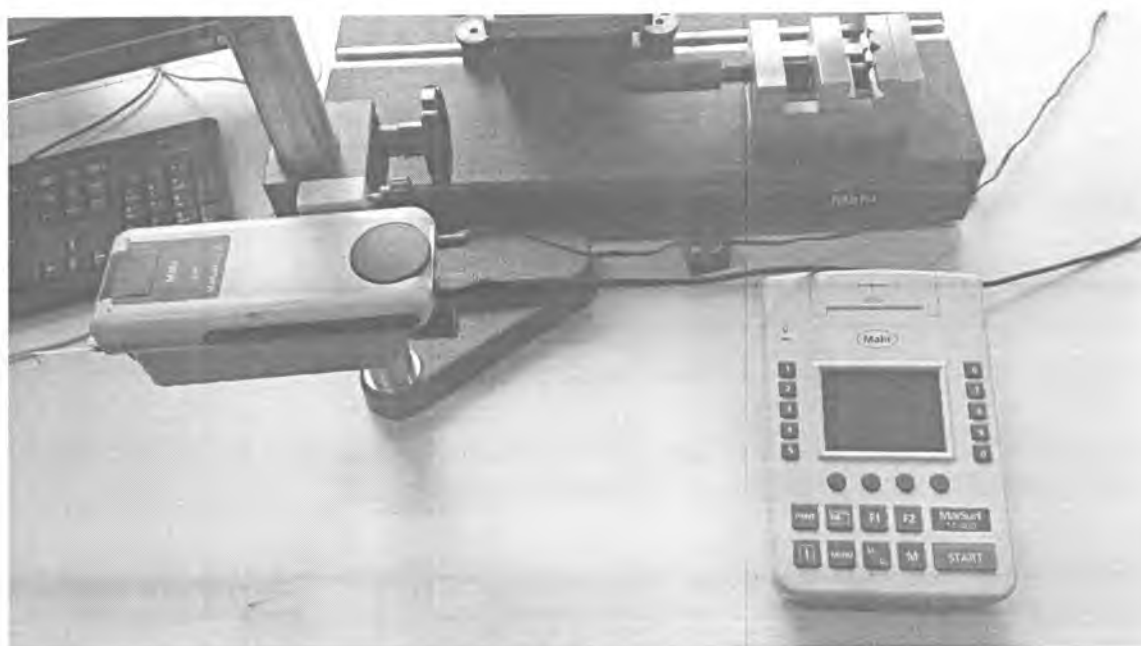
Внешний вид приборов для измерения шероховатости поверхности MarSurf M 400 в составе с RD 26
